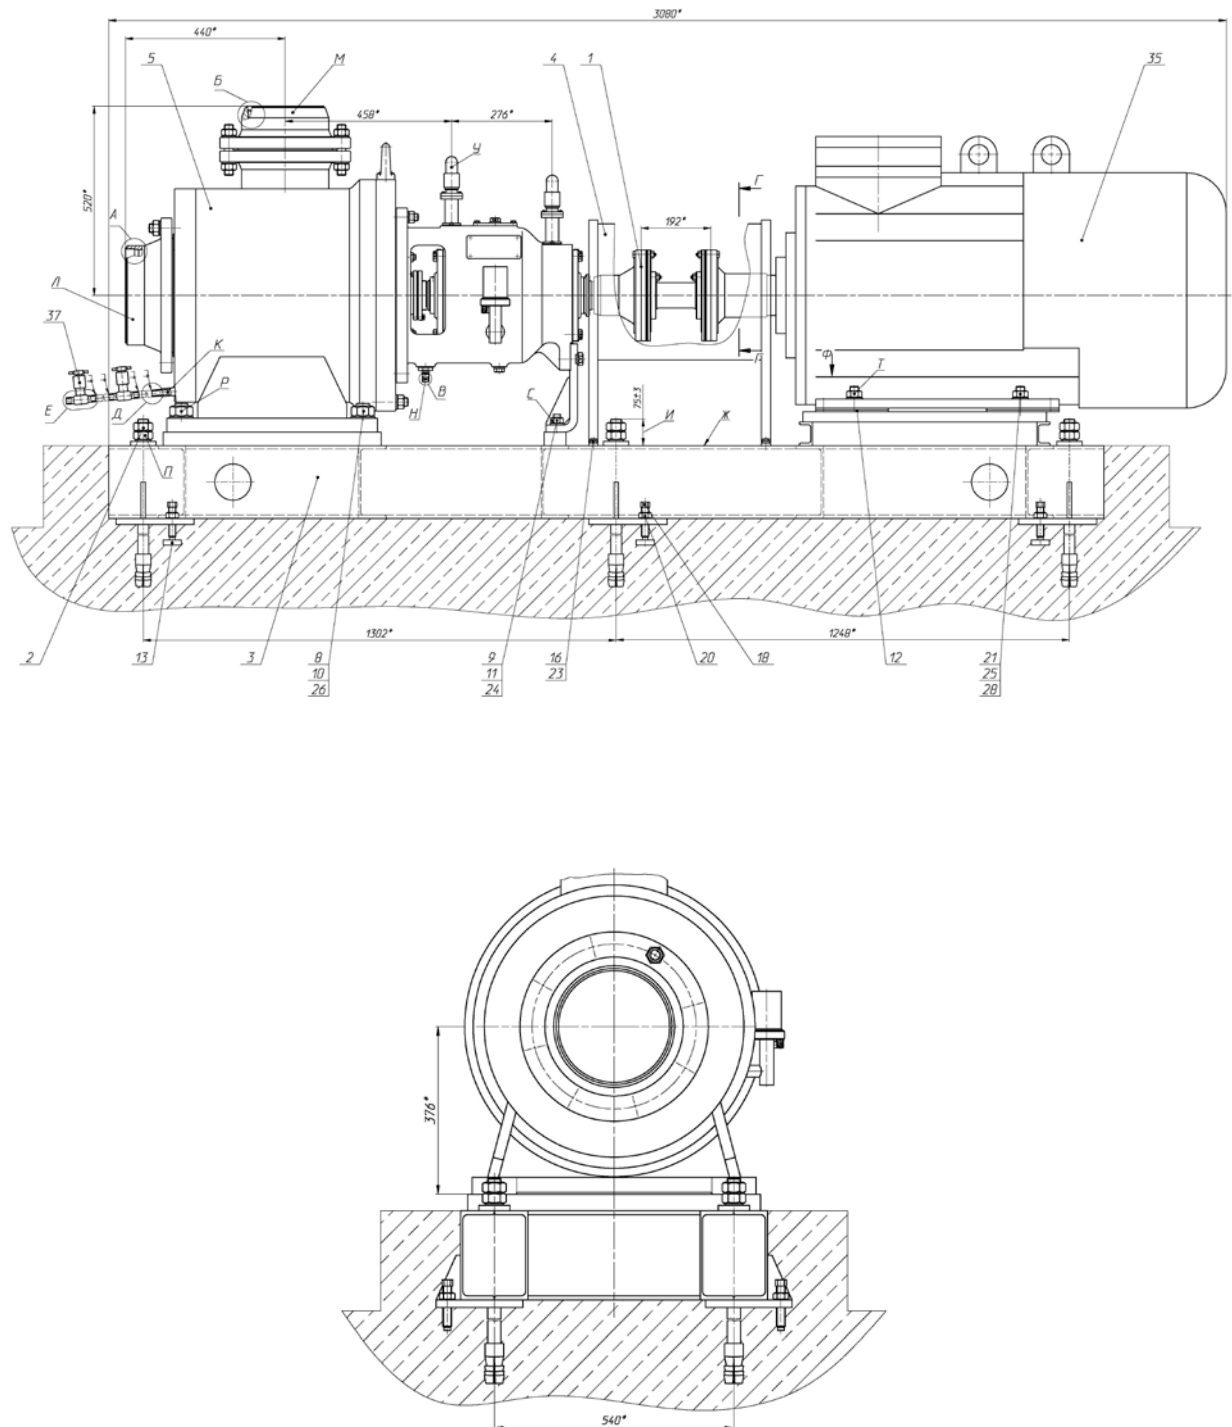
Габаритный чертеж спринклерного насоса
